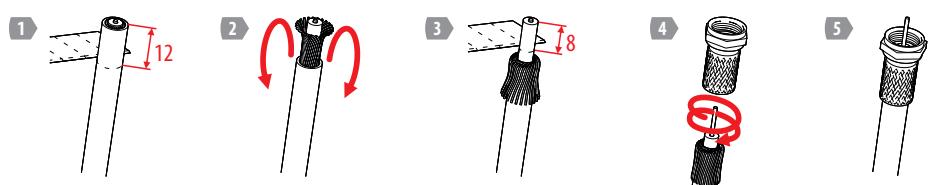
Разделка коаксиального кабеля и установка F-разъема
